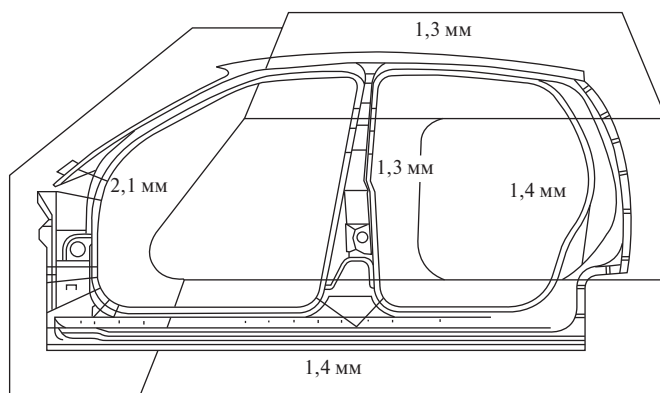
Заготовки, выполненные лазерной сваркой
